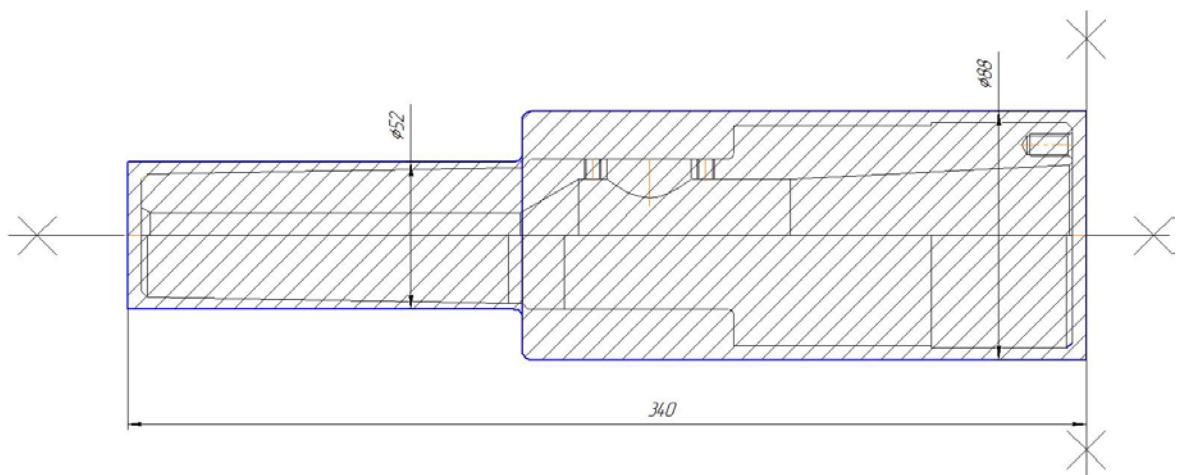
Ескіз заготовки деталі «Корпус борштанги»
